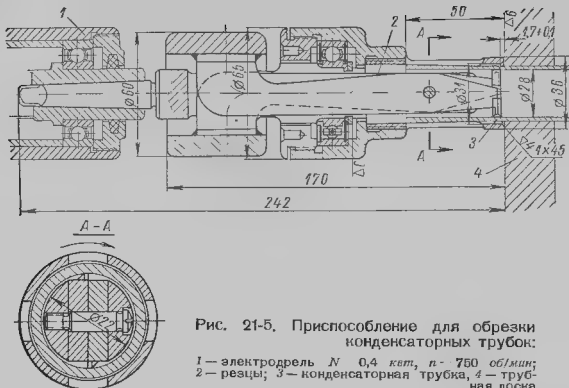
Приспособление для обрезки конденсаторных трубок:
